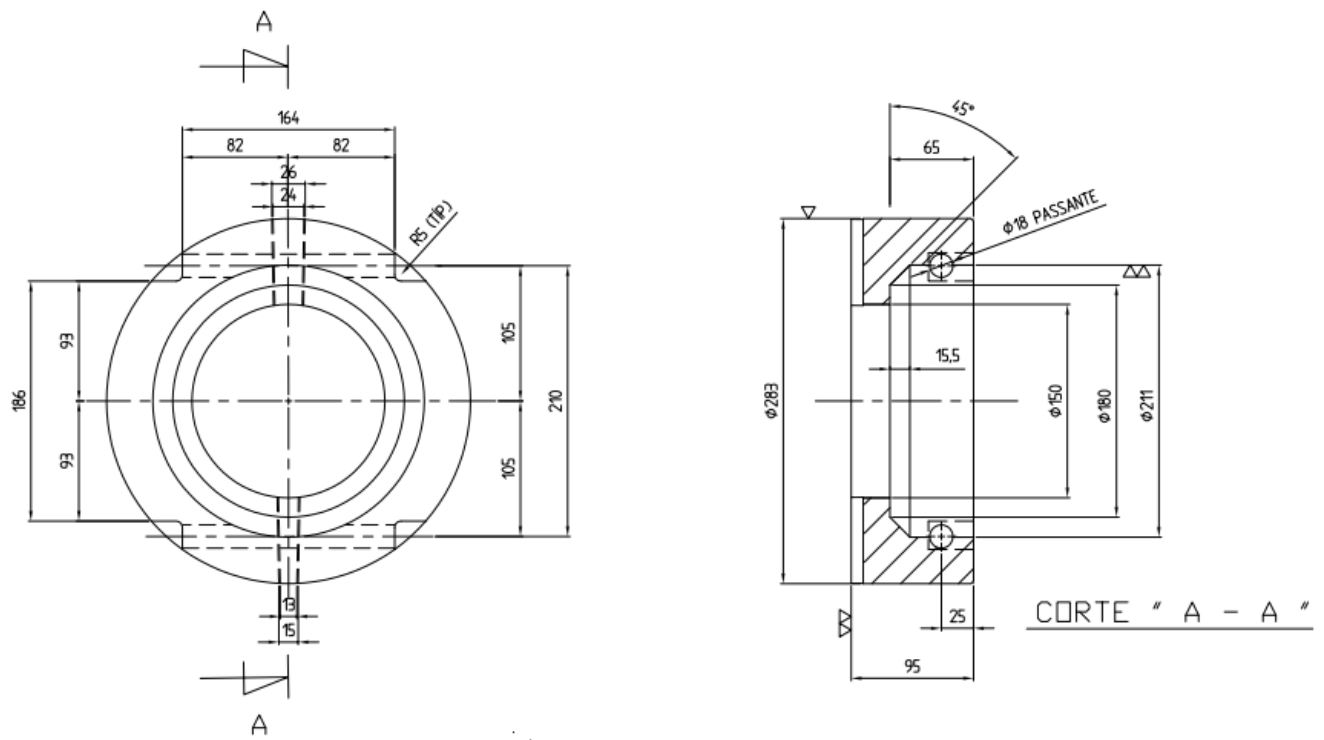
Desenho parte frontal da máquina de injeção usado para dimensionar o molde. [38]
